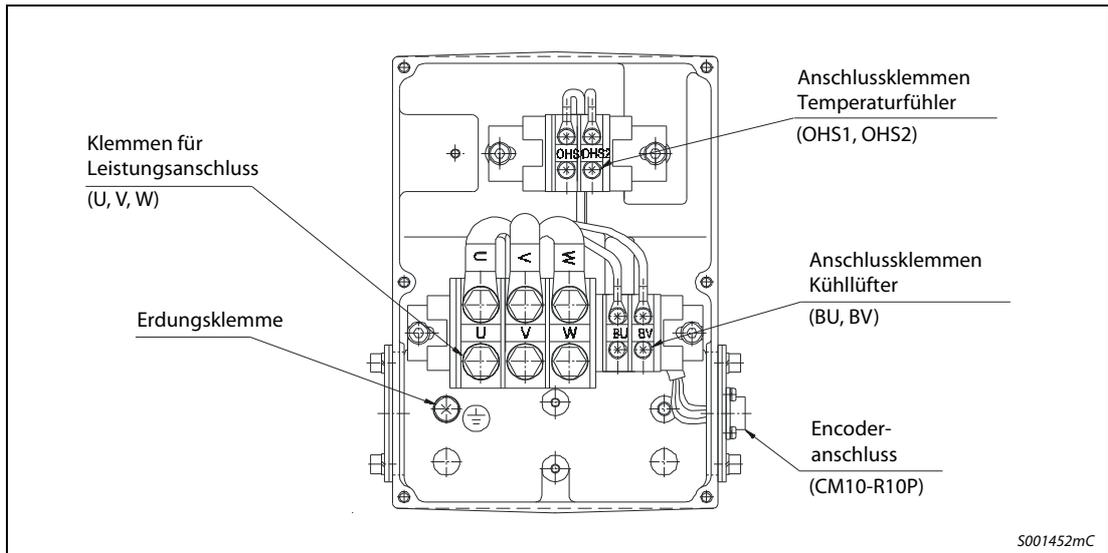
Klemmenkasten der Motoren HA-LP601(4)(B)/701M(4)(B)/11K2(4)(B)
